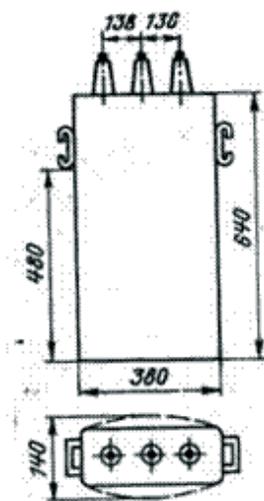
Внешний вид и размеры косинусного трехфазного конденсатора на напряжение 0,4 кВ
